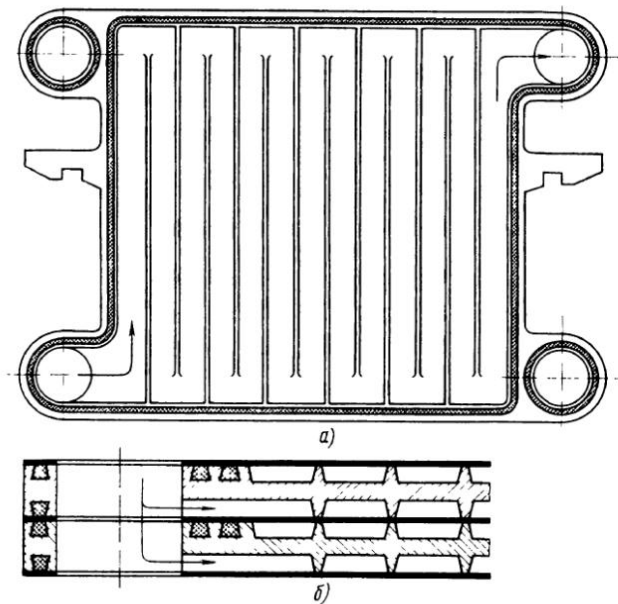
Пластины из бронзы с фрезерованными каналами:
